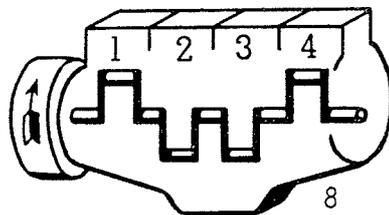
Zylinderbezeichnung beim Reihenmotor F AL 514
